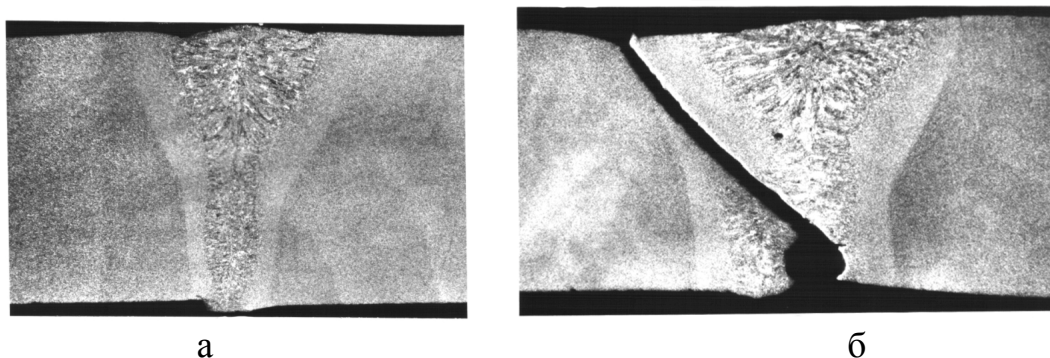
Фотография шлифа сварного шва: а) до гидравлических испытаний; б) после гидравлических испытаний (то же место).
